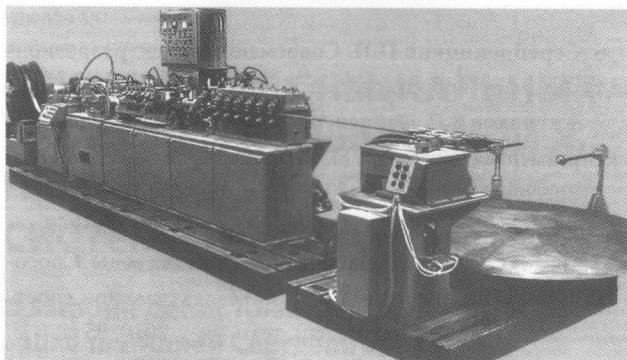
Стан аргонодуговой сварки труб АДСТ5-25-1М
